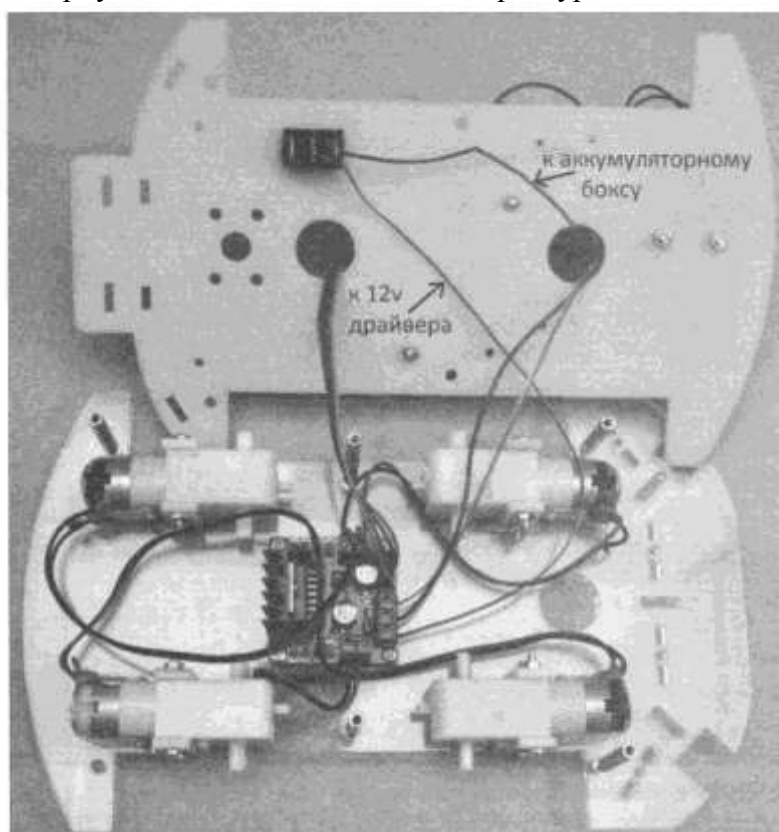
Подготовка верхней части корпуса робота к установке (прикреплены и выведены провода)
